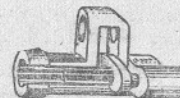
Штыковая трубка винтовки обр. 1891/30 г. прежних годов изготовления
